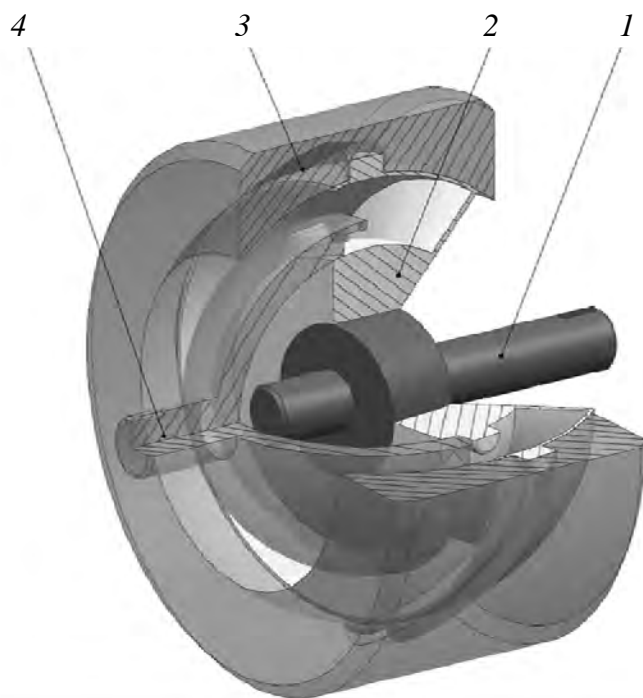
Компьютерная модель сферической роликовой передачи с двухрядным сателлитом: 1 – ведущий вал; 2 – сателлит, совмещенный с телами качения; 3 – корпус; 4 – ведомый вал
